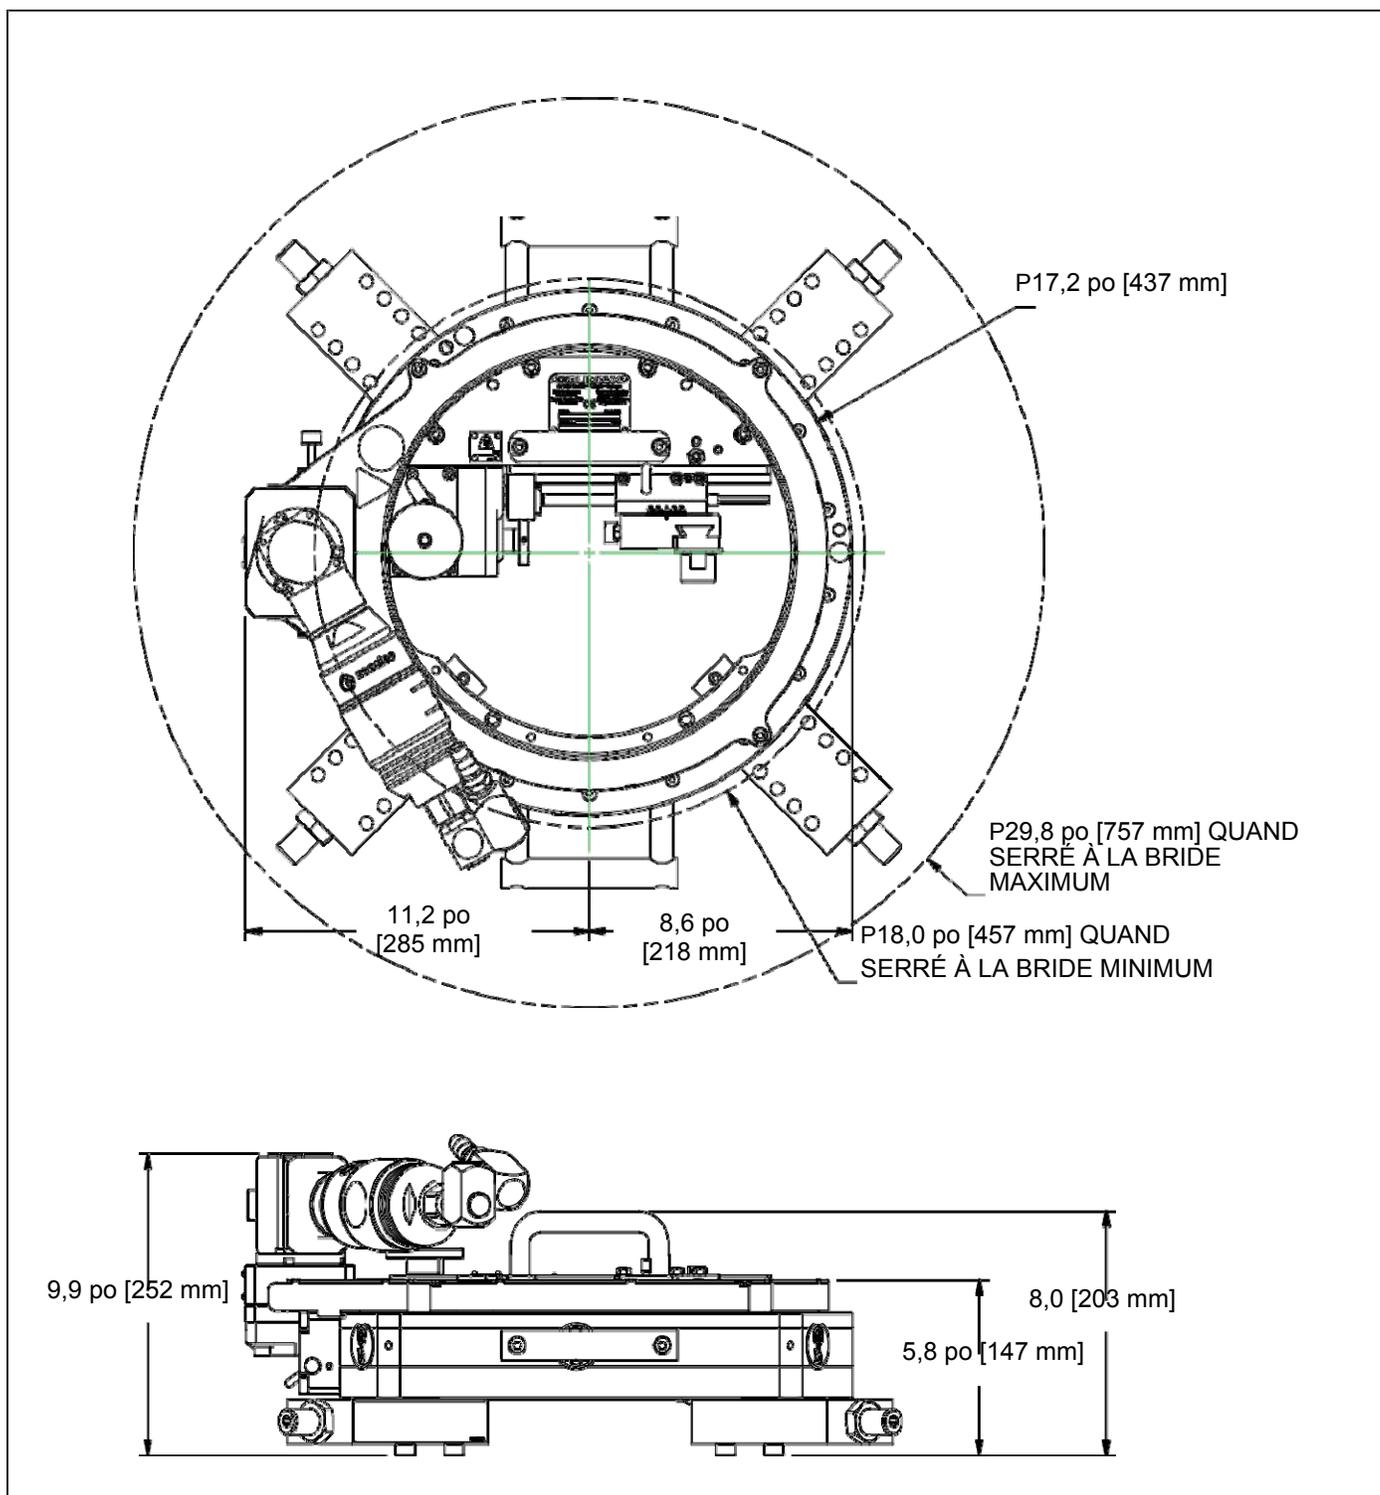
DIMENSIONS DE LA MACHINE FF2400
